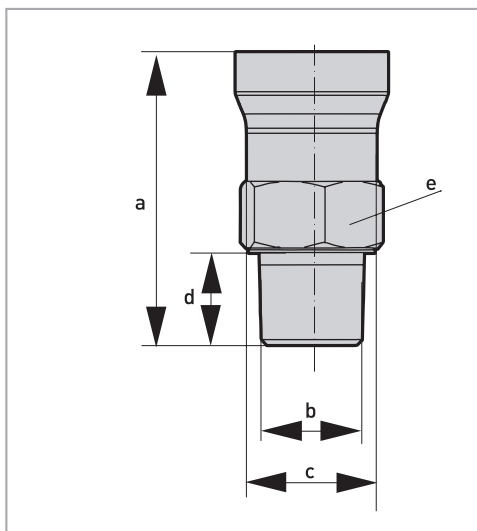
Резьбовое соединение ANSI 1/2" NPT с наружной резьбой
